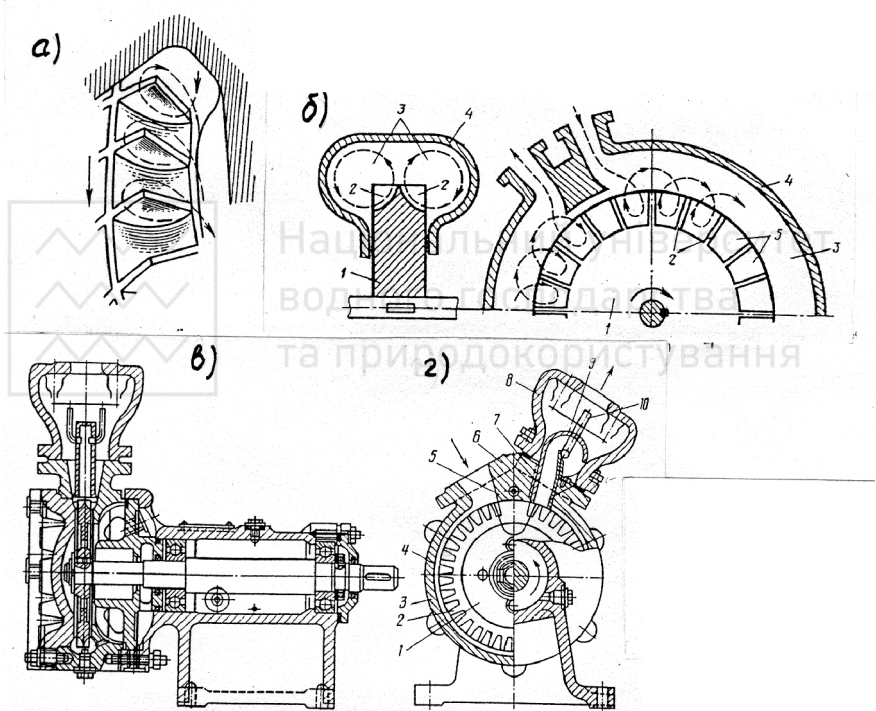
Боковоканальний насос: а) фрагмент робочого колеса; б) схема руху рідини; в), г) схема конструкції
